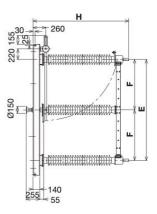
Dimensiones seccionador de columna giratoria 220 KV
